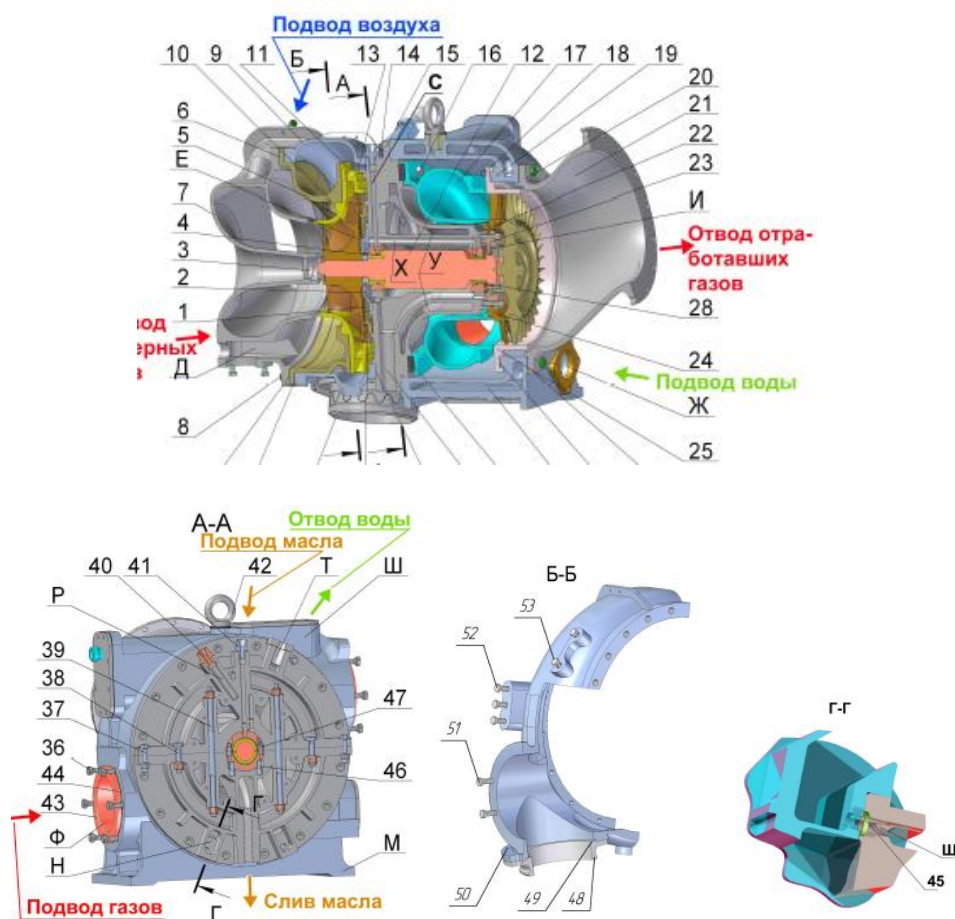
Турбокомпрессор: – лабиринт; 2, 29 – фланцы; 3 – пробка; 4 – подшипник опорно-упорный; 5, 39, 46 – шпильки; 6, 48 – проставки; 7 – входной патрубок; 8, 13, 14, 16, 18, 20, 36, 37, 38, 47, 48, 50, 51, 52, 53 – болты; 9 – улитка воздушная; 10 – прокладка регулировочная; 11, 25 – диффузоры; 12 – ротор; 15 – корпус средний; 17 – улитки газовые; 19 – корпус турбины; 21 – патрубок выпускной; 22 – штифт; 23 – втулка; 24 – аппарат со-пловой; 26, 27, 31, 34, 35, 44 – прокладки; 28 – подшипник опорный; 32, 45, 49 – кольца резиновые; 33 – труба резиновая; 40 – труба; 41 – шту-цер; 42 – рым-болт; 43 – труба жаровая; В, Е, И, К, У – полости; Д, Н, С, Т, Х – каналы; Ж, Р, Ф, Ш, Щ – отверстия; М – лапы.
